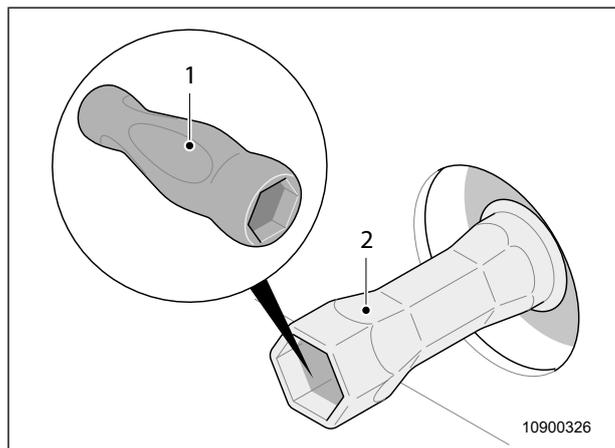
Mutter Heckleuchte mit Griff aus dem Bordwerkzeug
